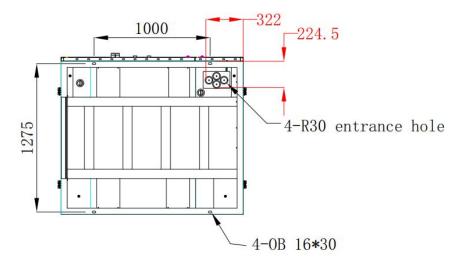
Estructura inferior del gabinete de la batería (vista inferior)
